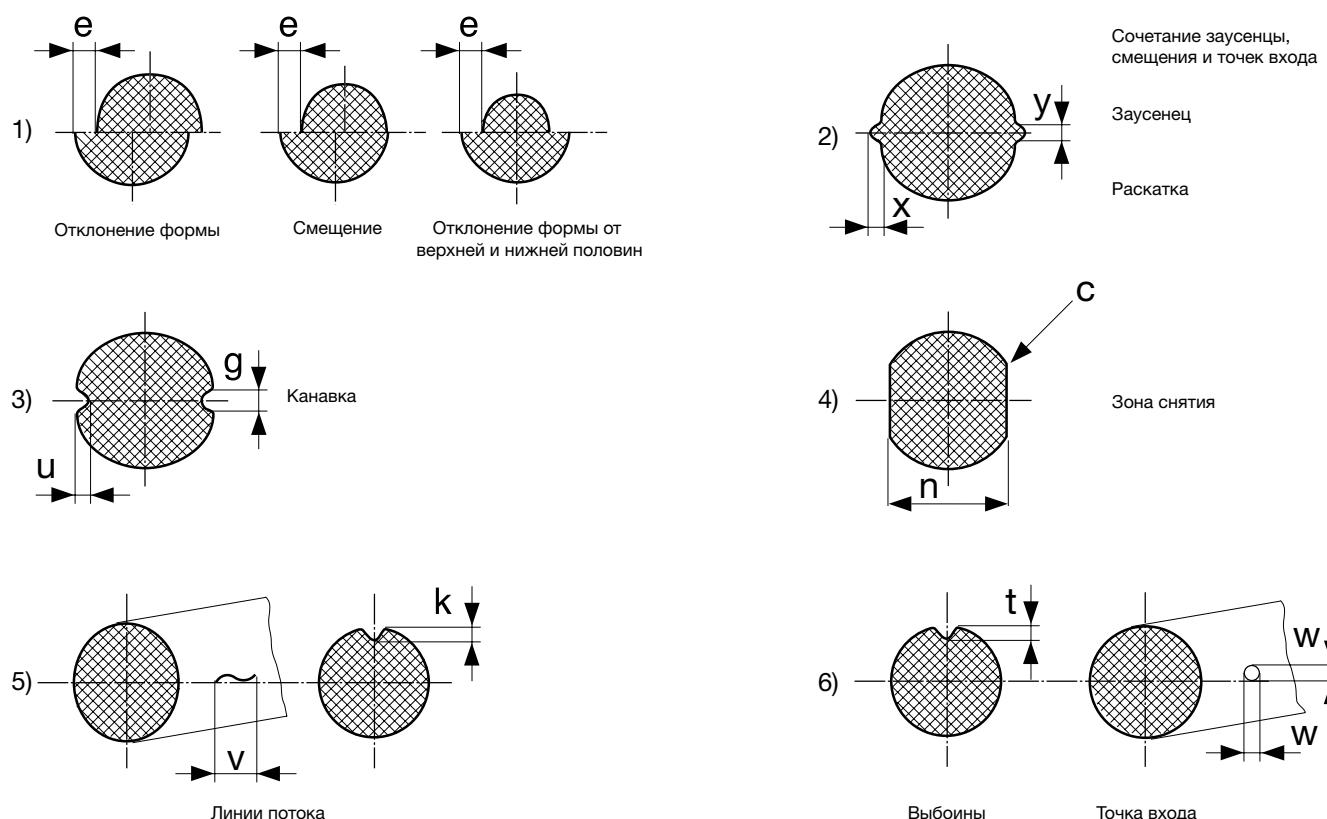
Дефекты отливки и обработки поверхности
